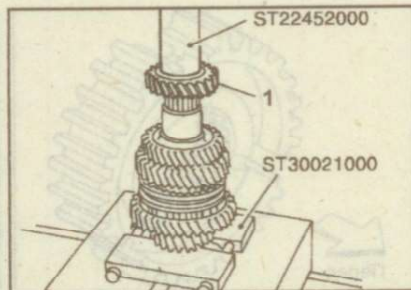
Установка шестерни 4-й передачи (1) на вторичный вал
